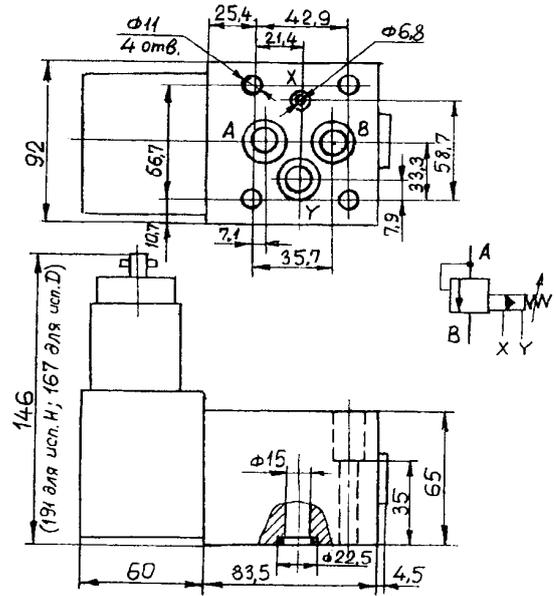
Клапан VBY10*1 Hydraulik-Ring
